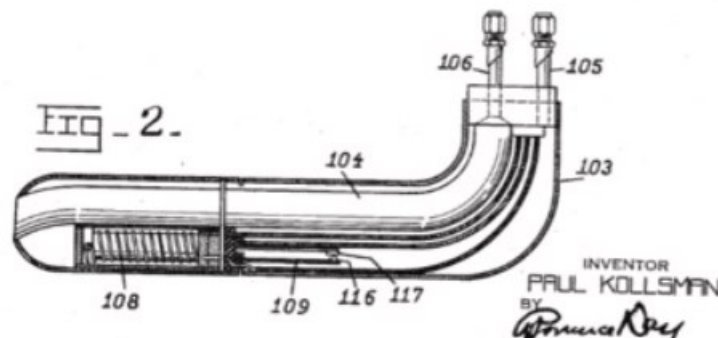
Brevetto Kollsman 1940 – R. Jackel et al., 2021
